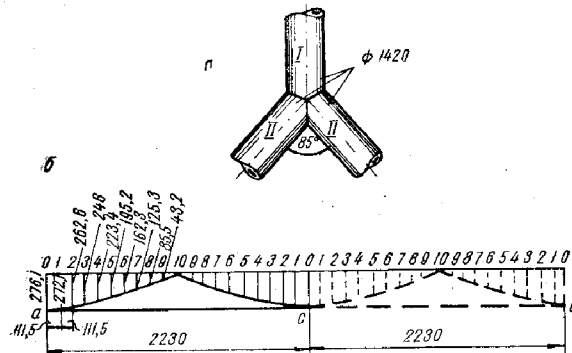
Сварной тройник разветвленный (штапы).
